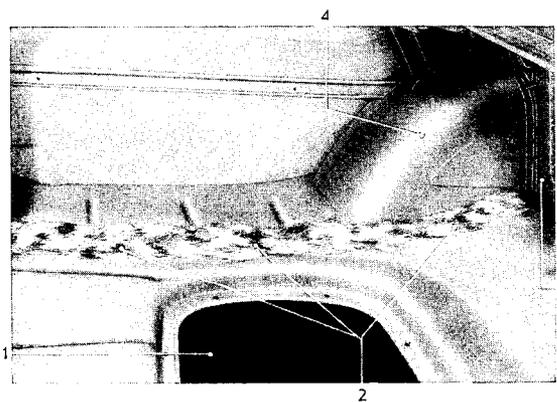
Bodenblech im Kofferraum blankgesäubert
